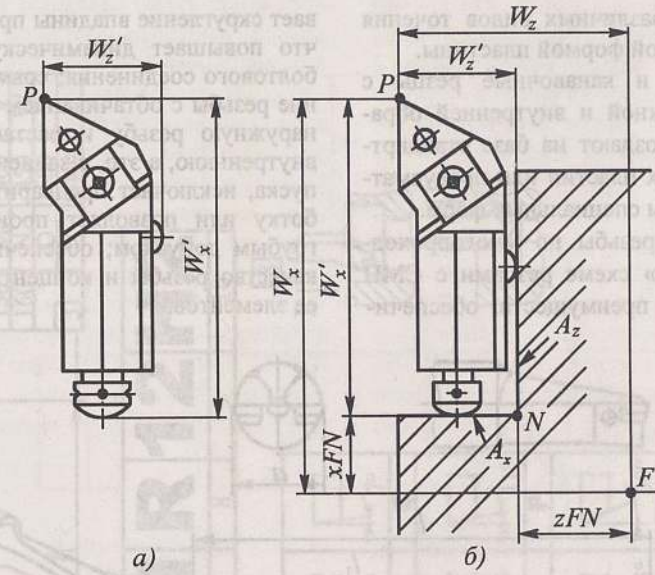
Державочный резец: а – схема резца; б – схема базирования резца в гнезде
